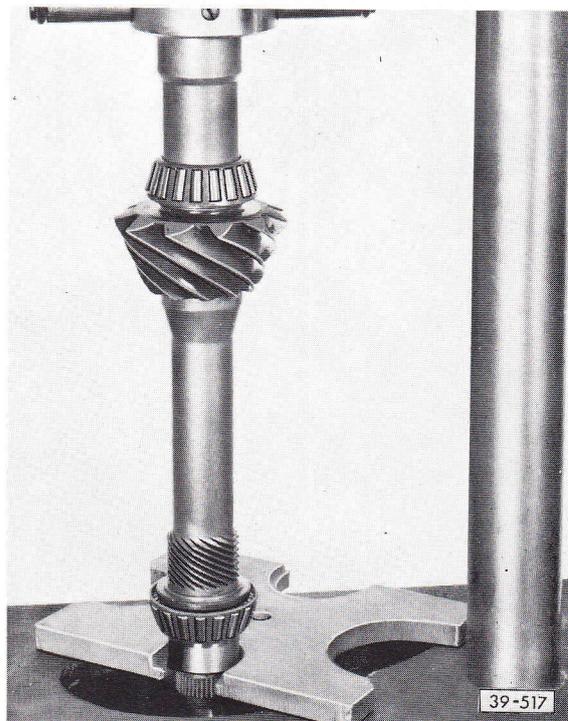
Bague intérieure de roulement à rouleaux coniques, chauffer à 100° C, mettre en place sur le pignon d'attaque et finir d'emmancher à la presse.
